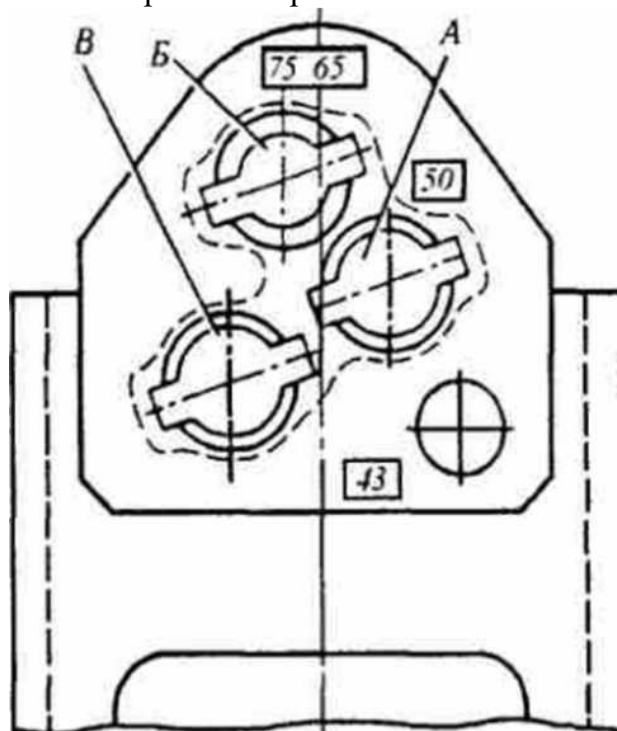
Упор съемный рельсосверлильного станка 1024В
